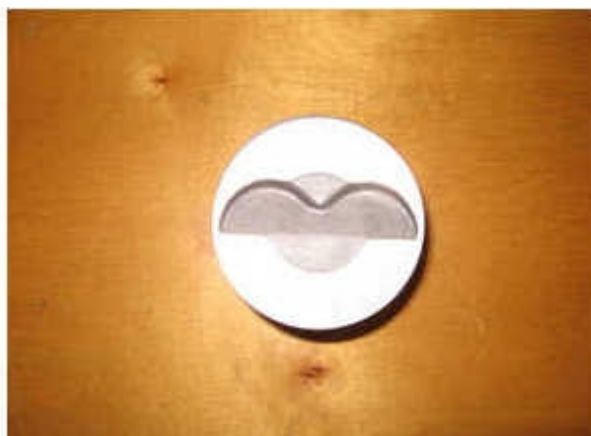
Поршень двигателя VAZ-2105 (вид со стороны камеры сгорания) - хорошо видны выемки под клапаны, которые положительно влияют и на оптимизацию процесса смесеобразования
